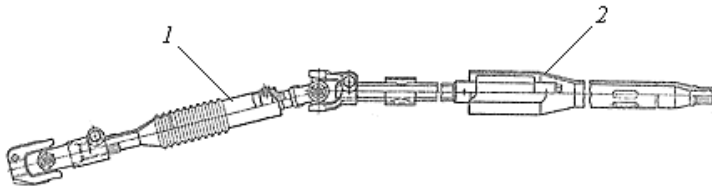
Вал рульового колеса, виготовлений фірмою «Lemforder metallvaren» для фірми «Volvo»:
